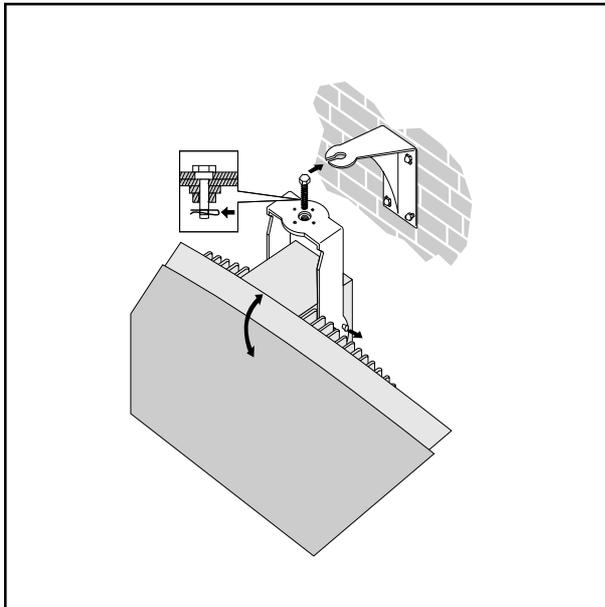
Подсоединение излучателя к кронштейну для настенного монтажа
